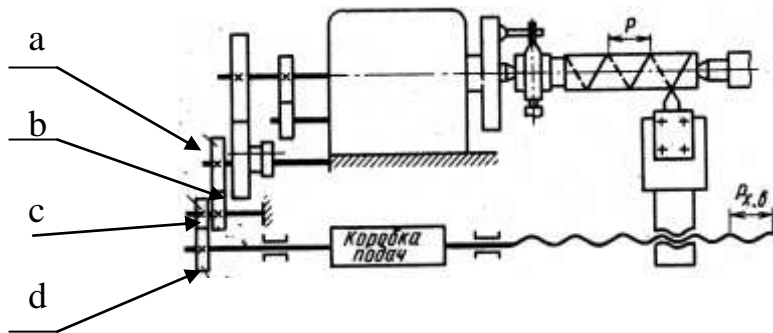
Резьбонарезная цепь токарно-винторезного станка.
